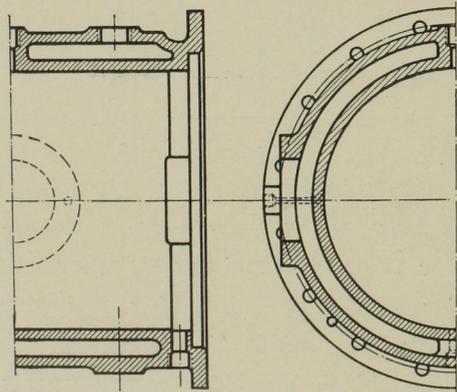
Niederdruckzylinder. Massst. 1:16.
